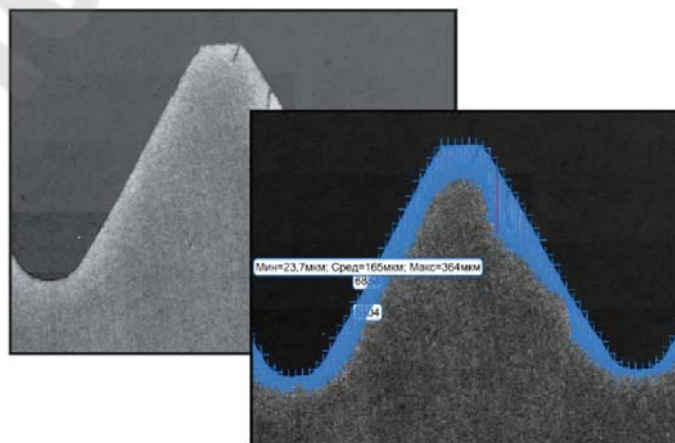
Обезуглероженный слой на поверхности зуба фрезы
